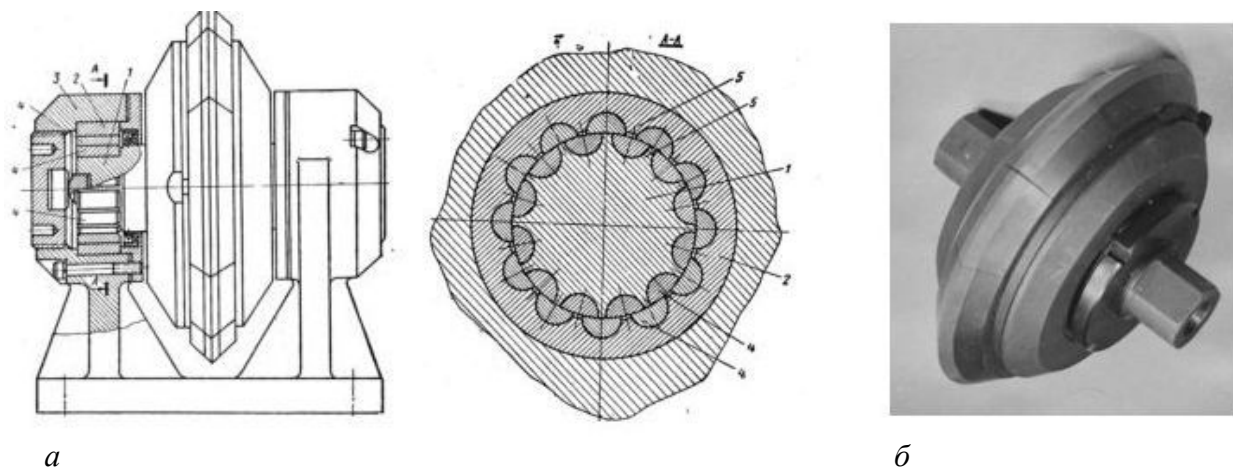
Конструкция клинового катка с твердосплавной опорой скольжения диаметром 200 мм (а) и его внешний вид (б): 1 – ось клинового катка; 2 – втулка; 3 – корпус; 4 – твердосплавная вставка; 5 – ребро жесткости
